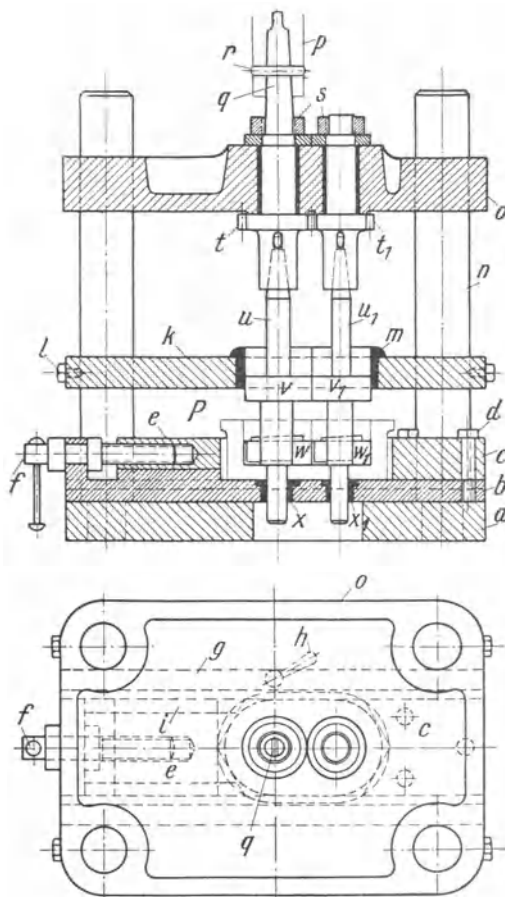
Bohrvorrichtung für Räderpumpengehäuse.
